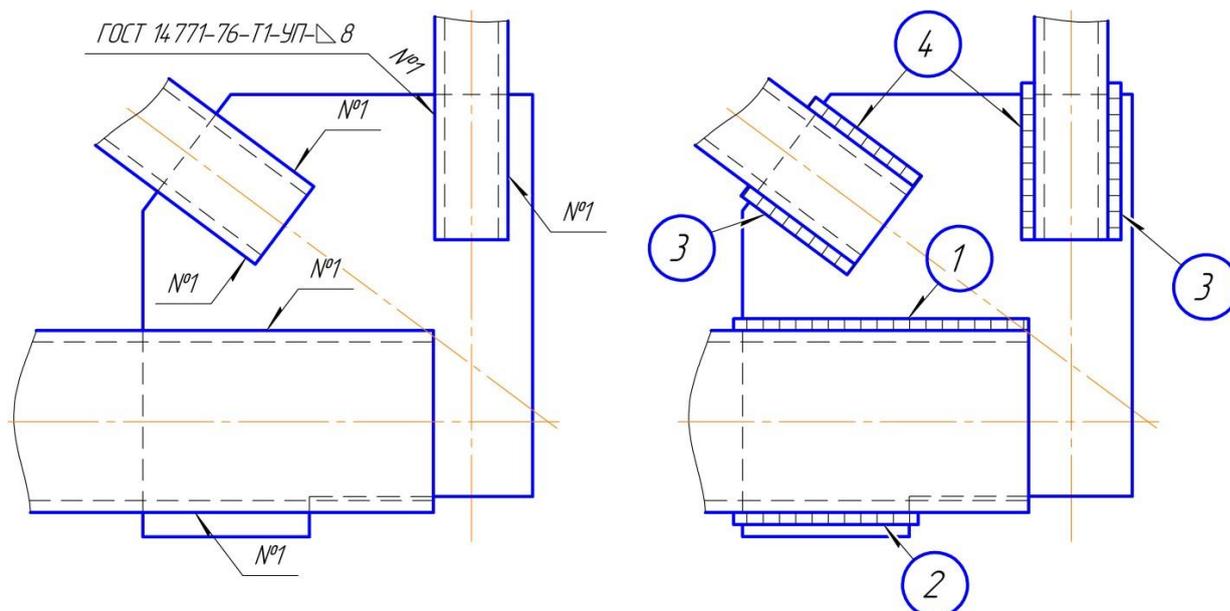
Последовательность наложения сварных швов узла нижнего пояса фермы
